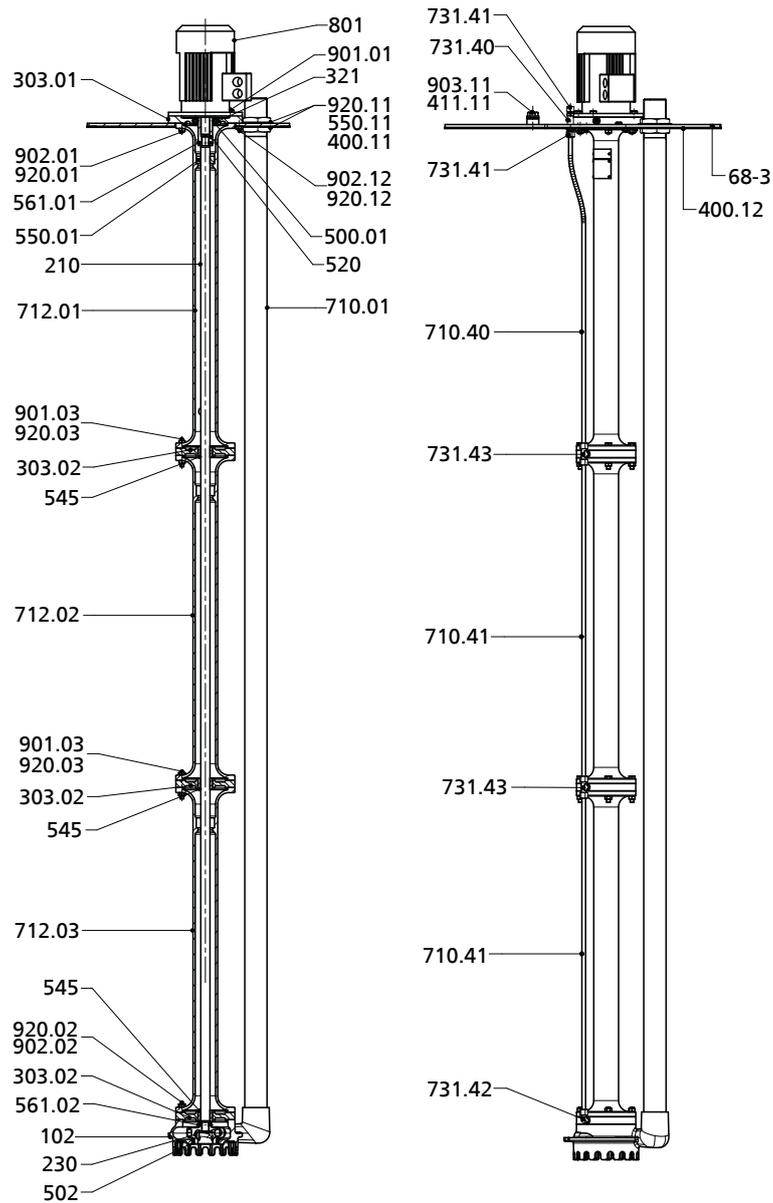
Сборочный чертеж МК, МКА - глубина установки 2800 мм - подача смазочной жидкости от постороннего источника
